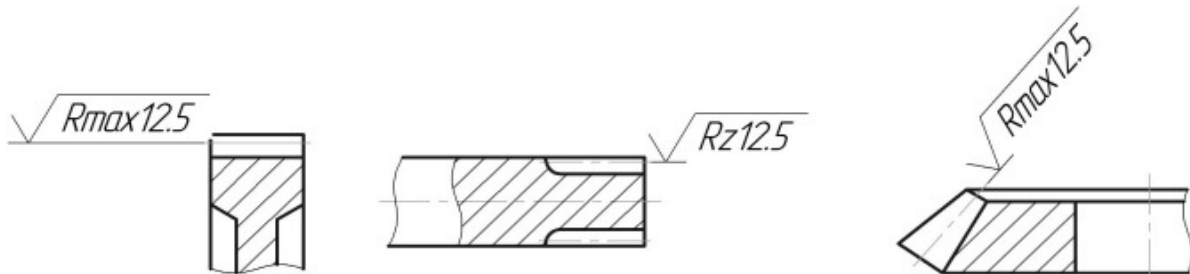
Примеры обозначения шероховатости рабочих поверхностей зубьев
